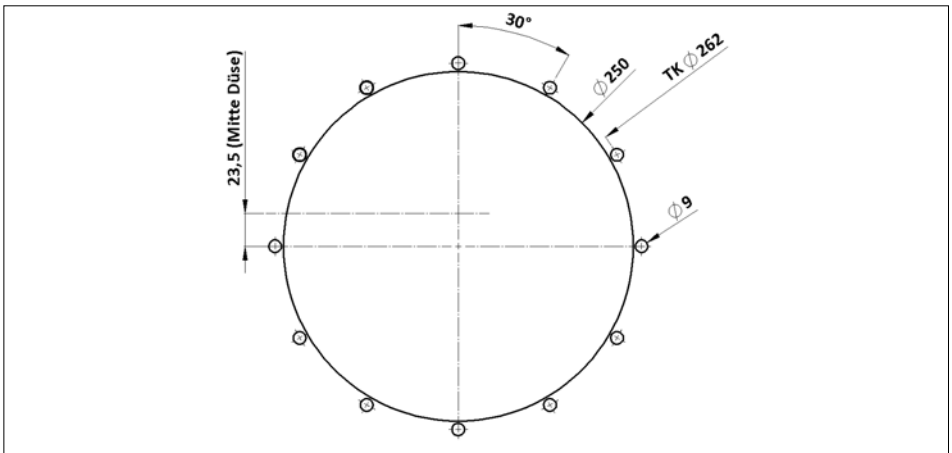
Bohrbild und Beckenausschnitt Fertigbecken
